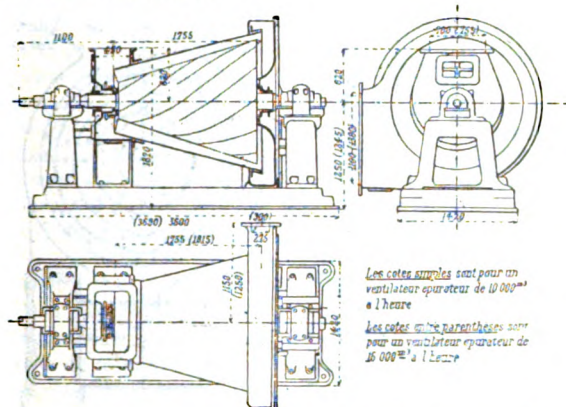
, 2 et 3. — Coupe, élévation et plan d'un épurateur centrifuge Schwarz.
